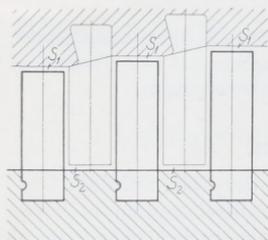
Ausschnitt aus einer Trommelturbine.
